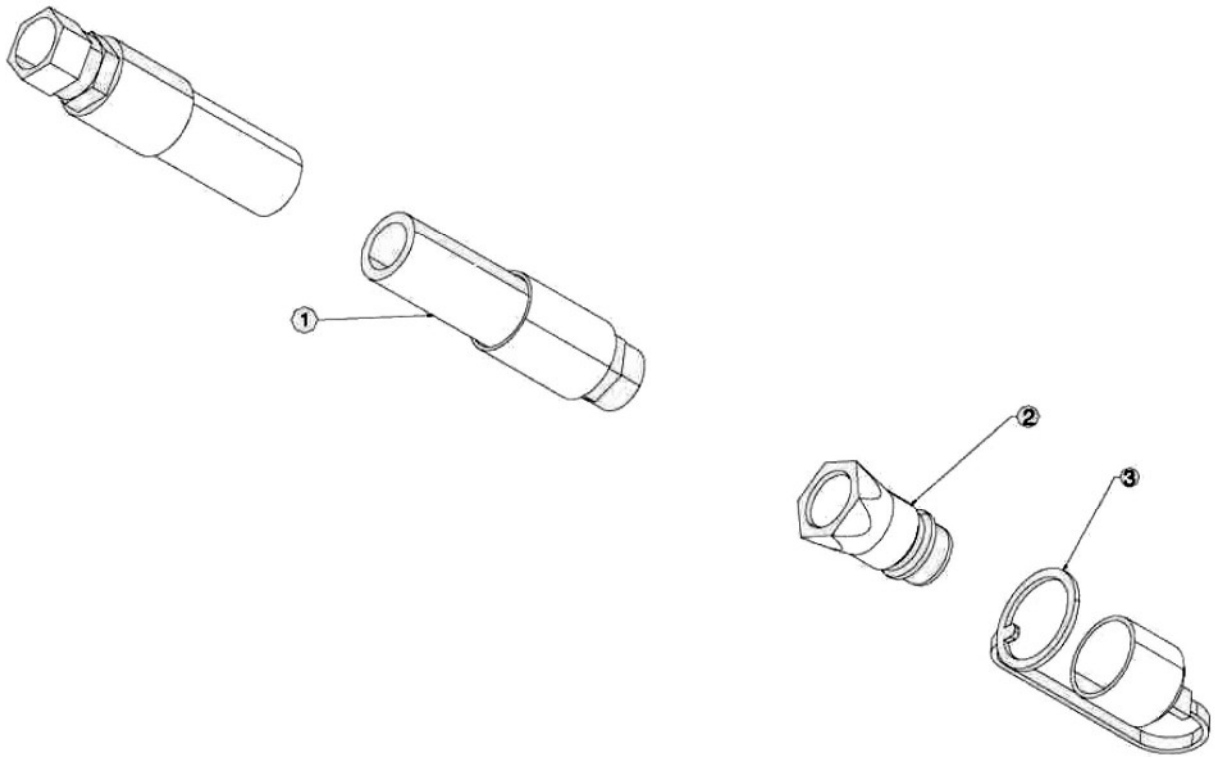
Чертеж сборки гидравлической линии - A7011-00
